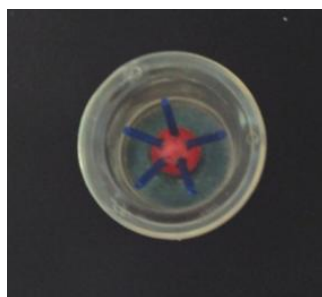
Padrões para fundição posicionados em anel de silicone sobre base formadora de cadinho.
